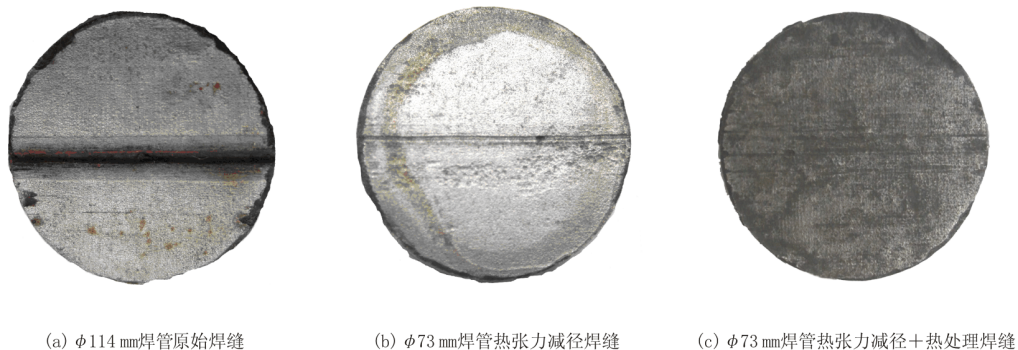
焊缝沟槽腐蚀形貌 8 \times
